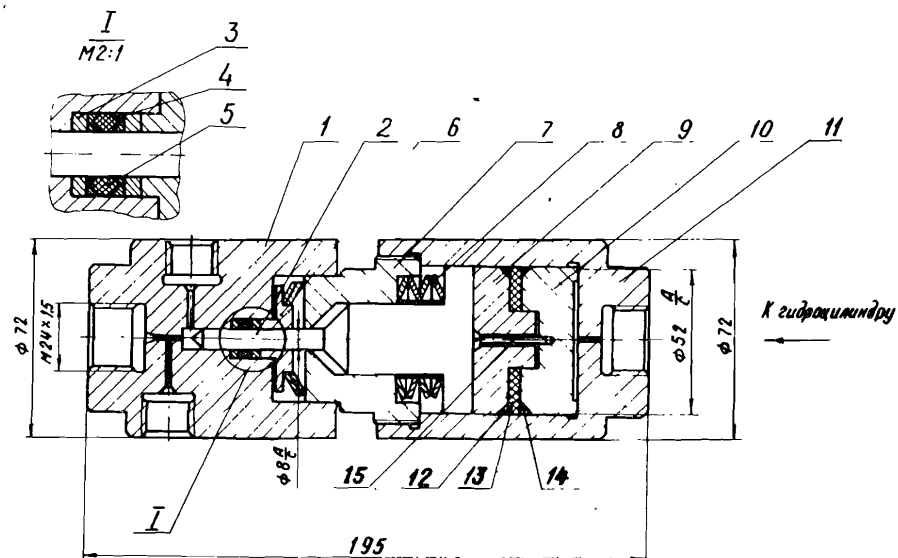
Принципиальная схема вентиля высокого давления: 1 - корпус вентиля, 2 - игла, 3 - стальное кольцо, 4 - кольцо латунное, 5 - фторопласт, 6 - грунд-букса, 7 - соединительная гайка, 8 - тарельчатые пружины, 9, 10 - поршень, 11 - корпус гидроцилиндра, 12, 13, 14 - система уплотнений поршня, 15 - винт поджимной.
